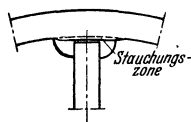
Querverbiegung bei Kehlnahtschweißung.
